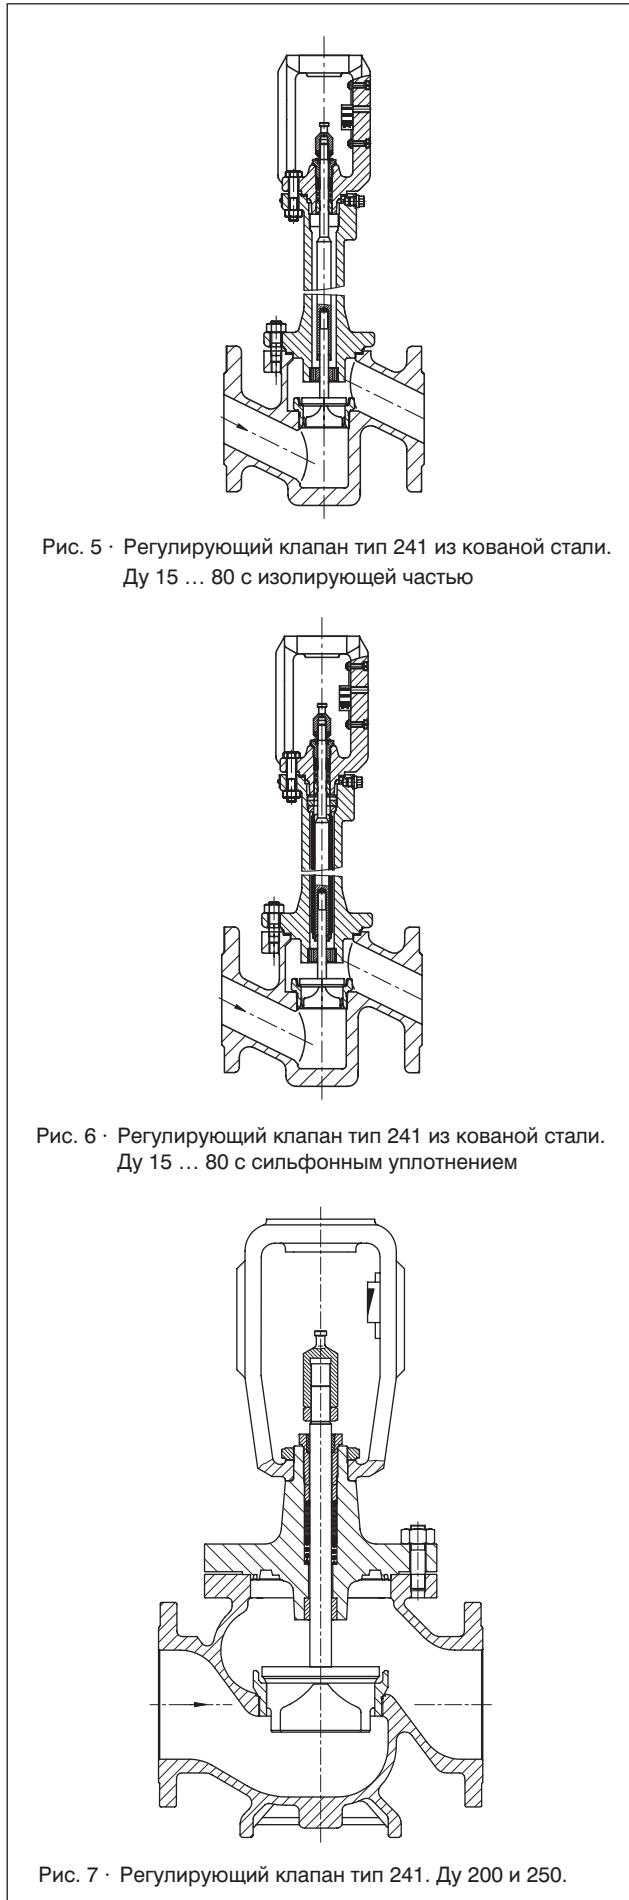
· Регулирующий клапан тип 241 из кованой стали.
